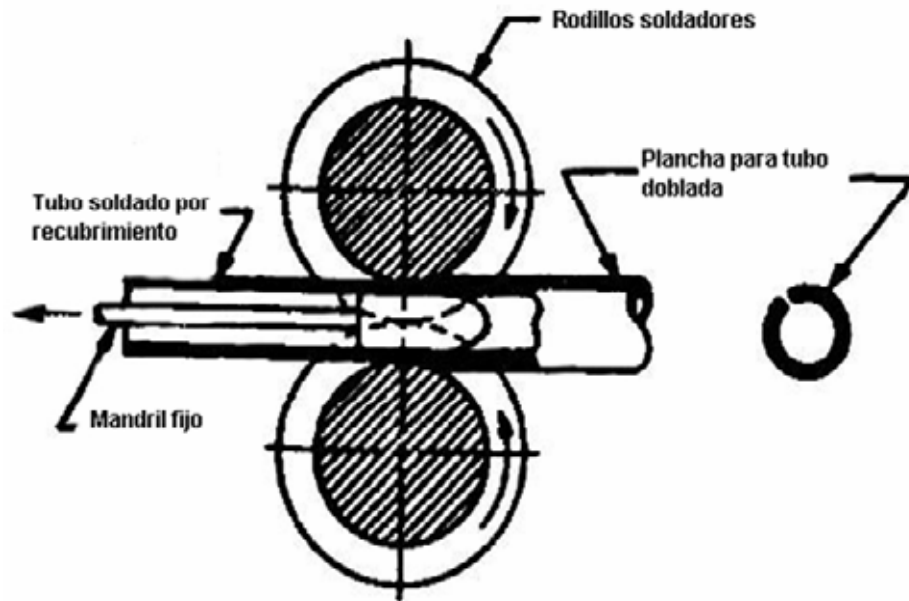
Tubo Soldado a Partir de Placa para Tubo
